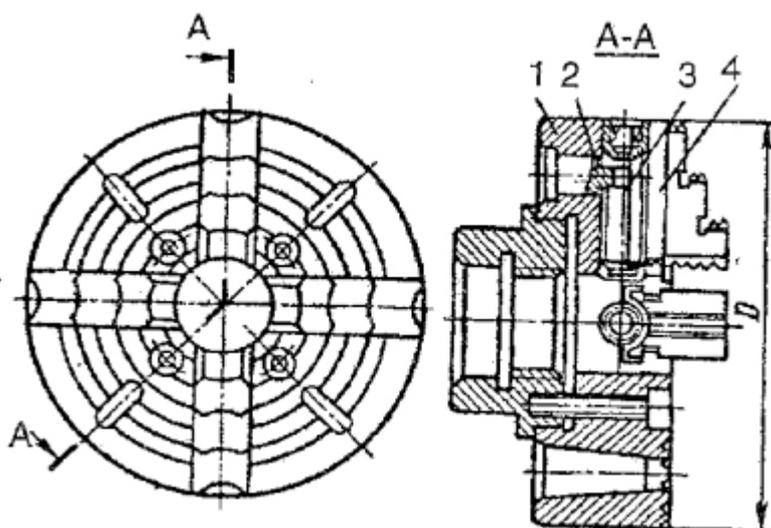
Конструкция четырехкулачкового патрона с независимым перемещением кулачков: 1 – корпус; 2 – сухарь; 3 – винт; 4 – кулачок.
